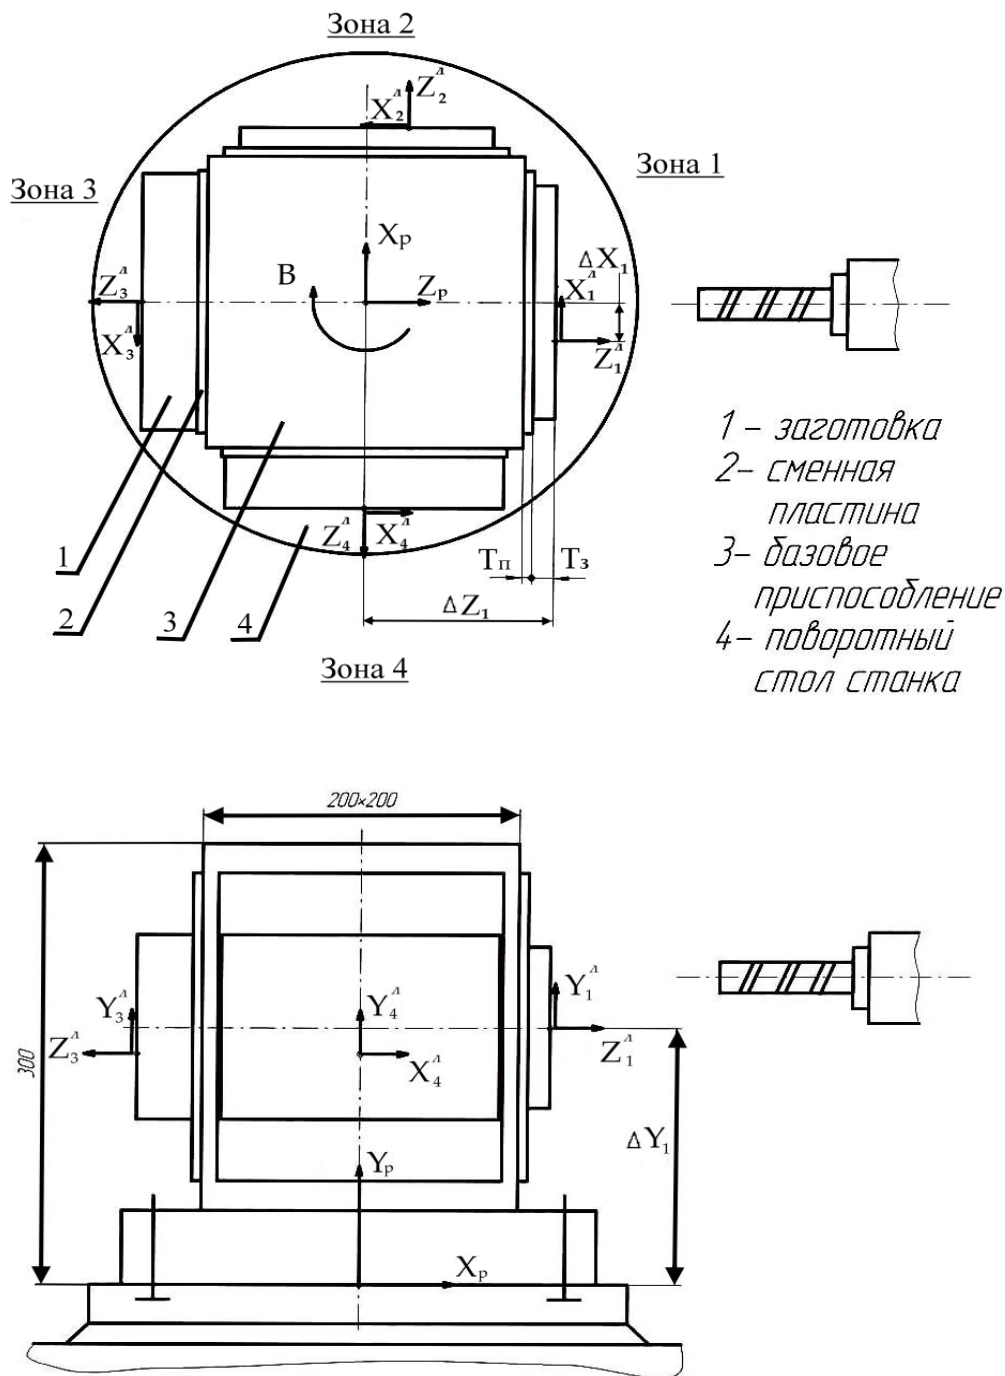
Типовая схема компоновки технологической системы станка с привязкой обрабатываемых заготовок к базовому приспособлению
